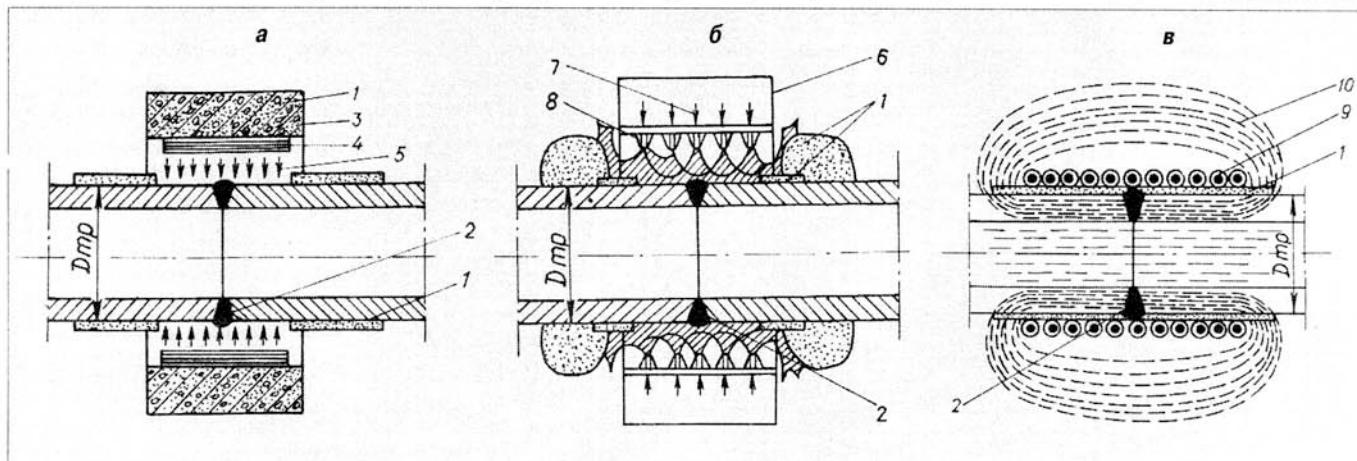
Схема нагрева сварных соединений трубопроводов при местной термообработке: электронагревателем сопротивления (а); газопламенным нагревом (б); индукционным методом (в); 1 – теплоизоляция; 2 – сварной шов; 3 – корпус электронагревателя; 4 – нагревательный элемент; 5 – тепловой поток; 6 – корпус кольцевой горелки; 7 – горючий газ; 8 – пламя; 9 – индуктор; 10 – магнитный поток
